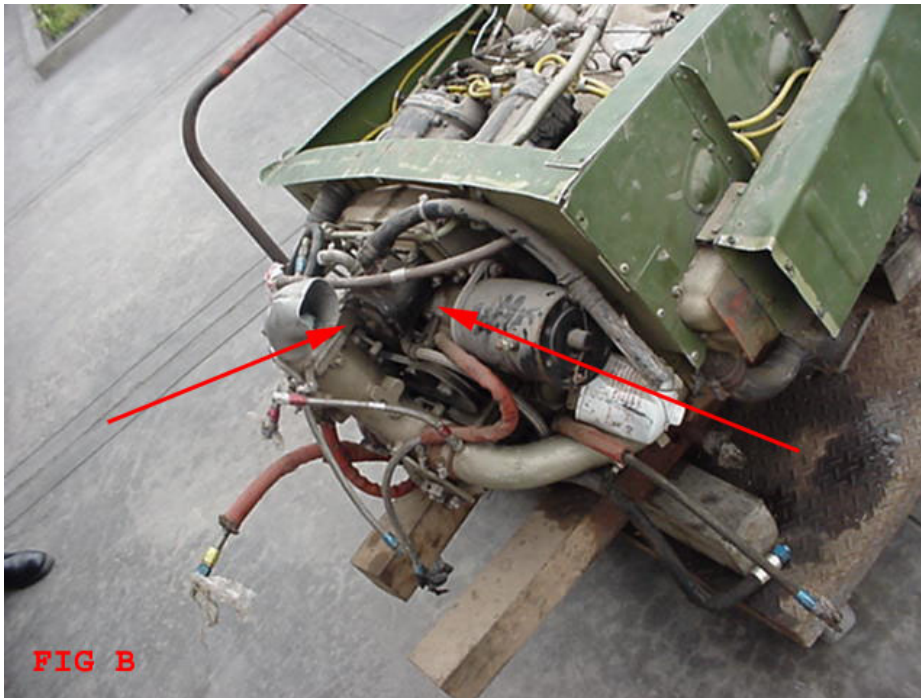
FIG B. detalle de la bomba de combustible en la parte posterior del motor.
